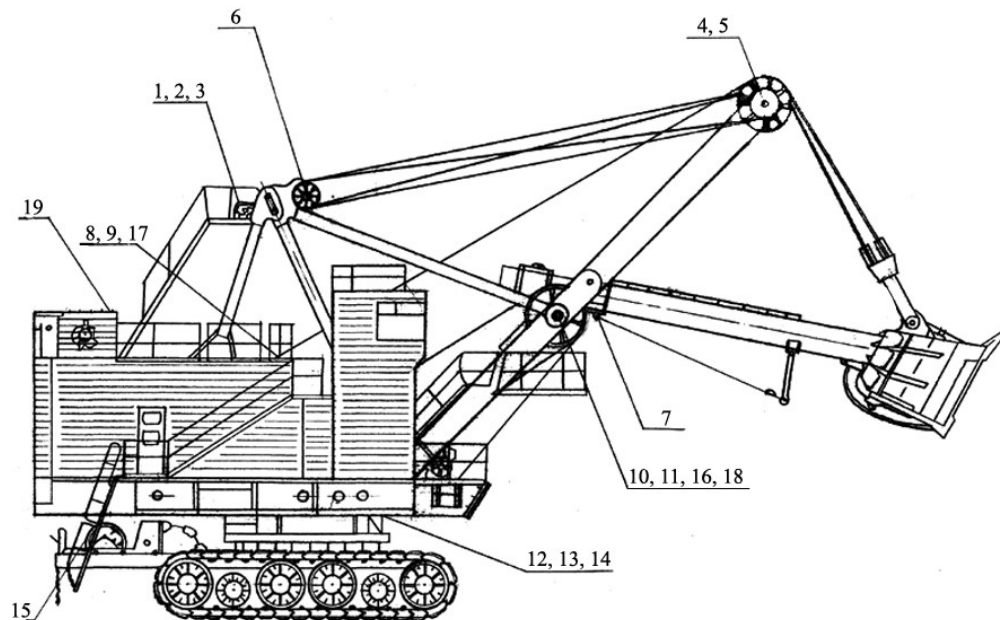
Схема смазки экскаватора ЭКГ-5У
